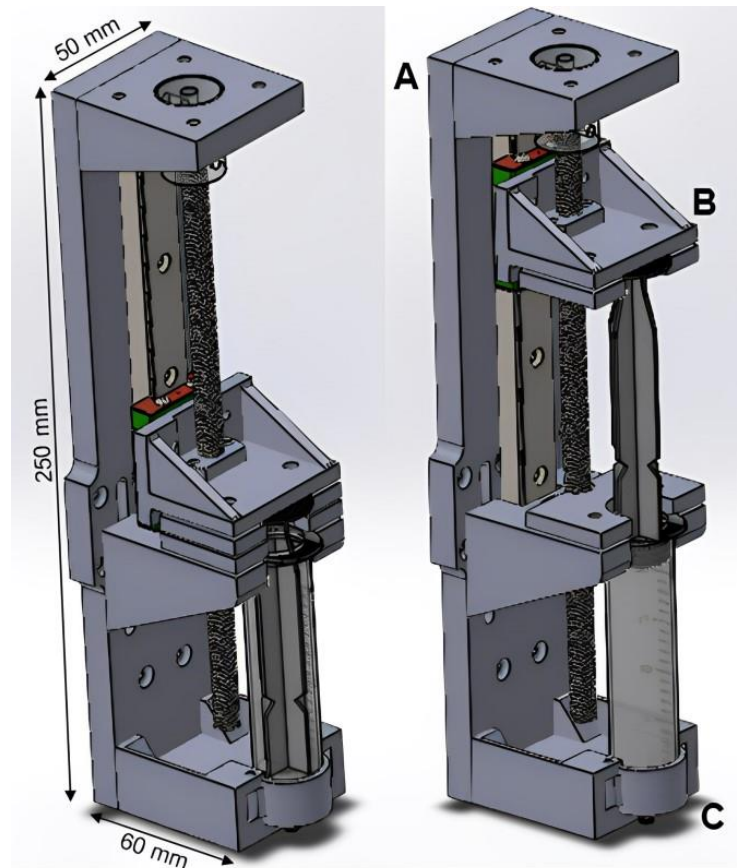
Conjunto montado do módulo de seringa e principais componentes; A) Peça de base; B) Peça de movimentação na guia e C) Cilindro de suporte inferior da seringa.
